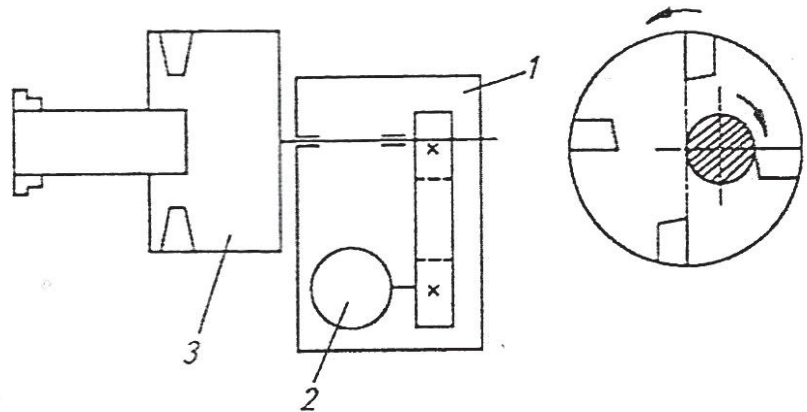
Схема нарезания резьбы на токарном станке «вихревым способом»
